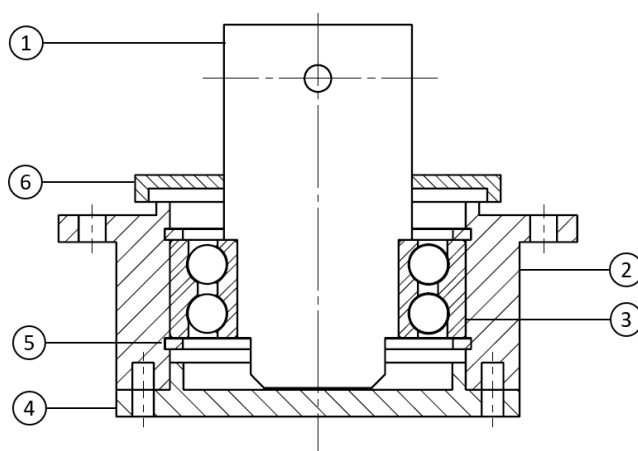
Proposta para a fixação do mastro com a tampa soldada ou colada ao veio: 1 - Veio; 2 - Caixa de rolamentos; 3 - Rolamento; 4 - Tampa inferior; 5 - Anel elástico; 6 - Tampa superior
